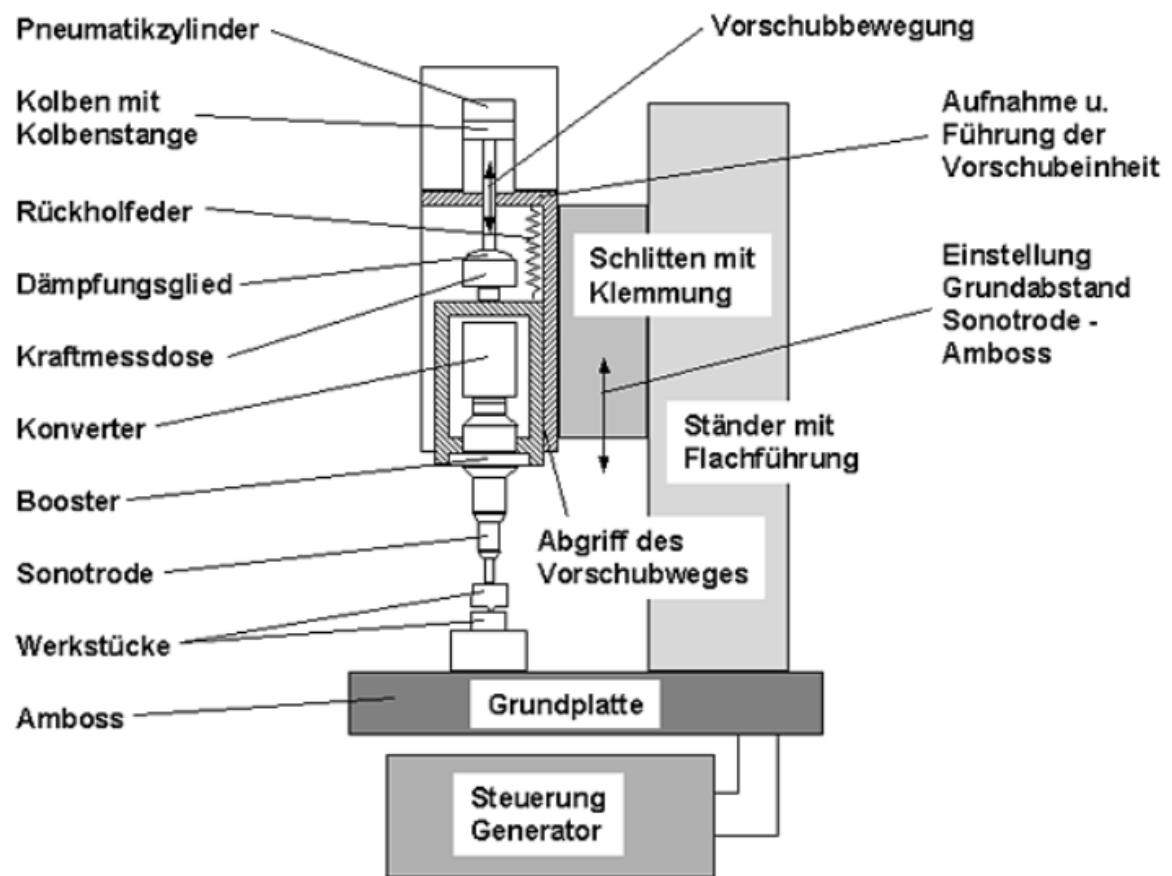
Aufbau einer Ultraschallschweißmaschine [44]
